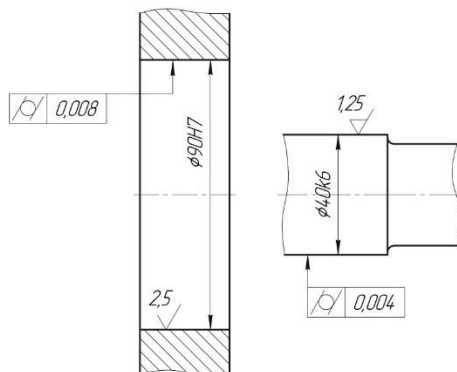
Обозначение па чертежах допусков размеров и формы деталей сопрягаемых с кольцами подшипников
